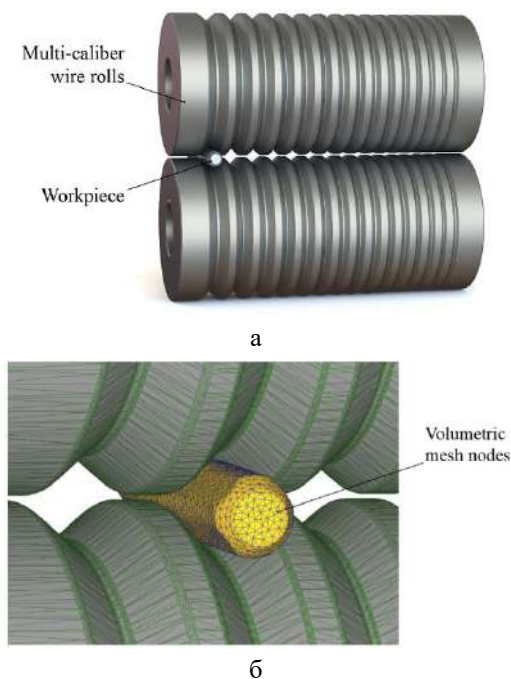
Общий вид модели сортовой прокатки прутков: а – модель валков в SolidWorks; б – модель процесса прокатки заготовки с конечно-элементной сеткой в Deform-3D
